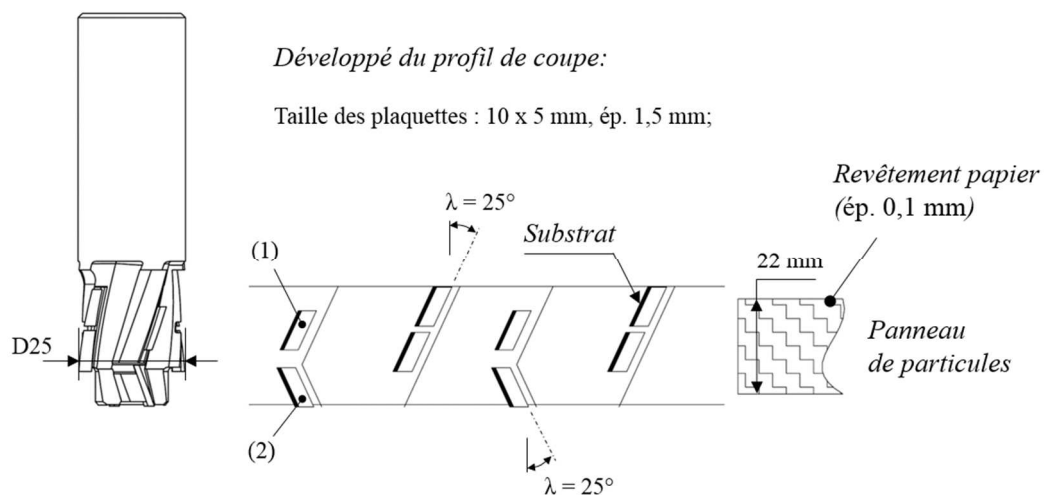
Géométrie de la fraise d'usinage à plaquettes céramique Z2+2
